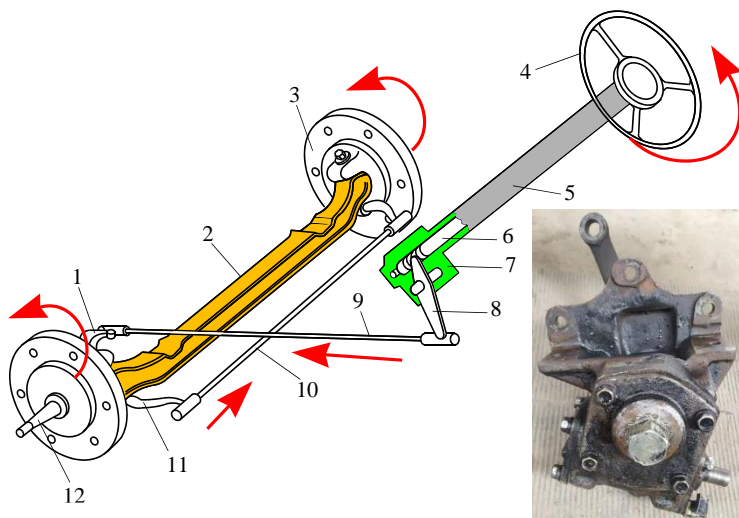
Схема механізму керування та загальний вигляд рульового механізму ГАЗ-3307: 1 – важіль поздовжньої тяги; 2 – передня балка; 3 – поворотний кулак; 4 – рульове колесо; 5 – рульова колонка; 6 – рульовий вал; 7 – рульовий механізм; 8 – сошка; 9 – поздовжня тяга; 10 – поперечна тяга; 11 – важіль поперечної тяги; 12 – вісь рульового колеса
